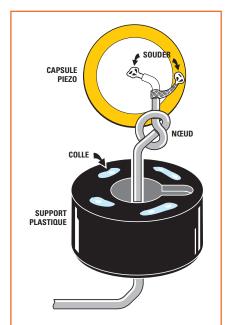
Pour effectuer le montage du disque piézoélectrique sur son support plastique, il faut souder l'âme du câble coaxial au centre du disque céramique et la tresse à son bord externe. Quand ces soudures sont terminées, vous pouvez fixer le disque sur son support avec de la colle ou du ruban adhésif double face.
